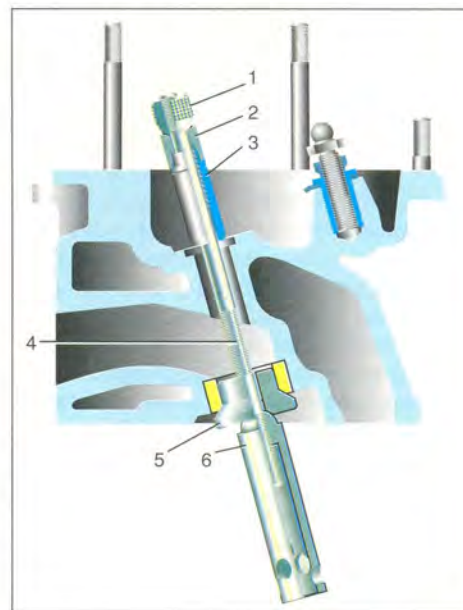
Запрессовка направляющей втулки клапана без применения ударов: 1 – гайка верхняя; 2 – оправка; 3 – направляющая втулка; 4 – шпилька; 5 – упор в седло клапана; 6 – гайка нижняя.
